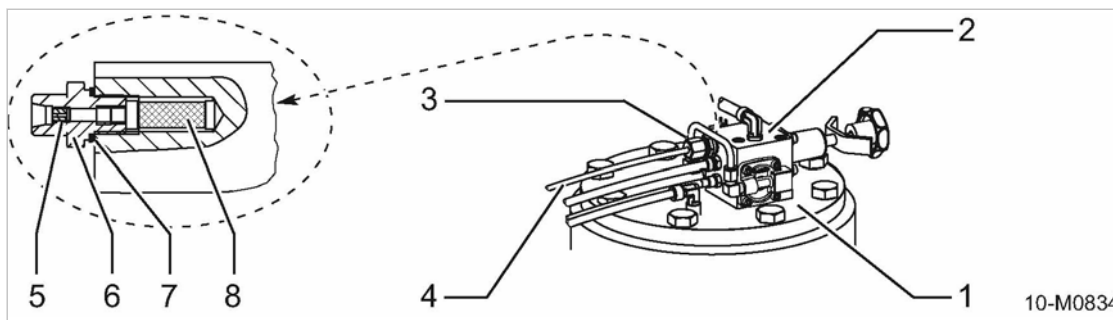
Vedlikehold av smussfanger på oljeutskillerbeholder
